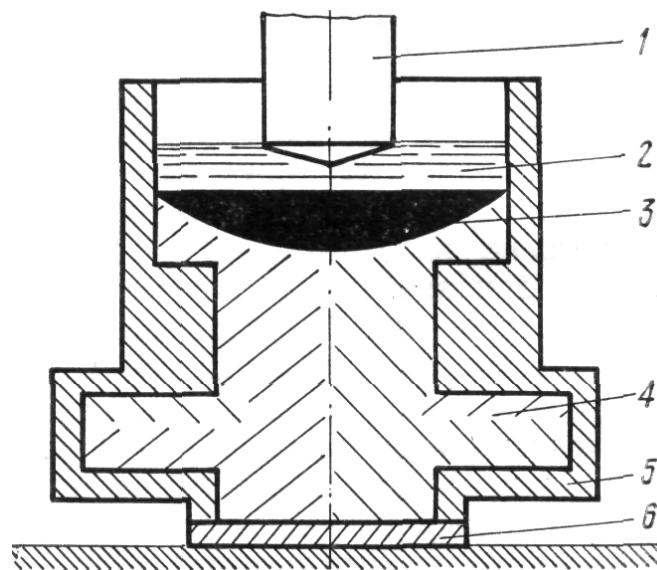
Схема електрошлакового лиття: 1 - електрод, що витрачається; 2 - шлакова ванна; 3 - металева ванна; 4 - отливка; 5 - форма ливарні; 6 - піддон.
